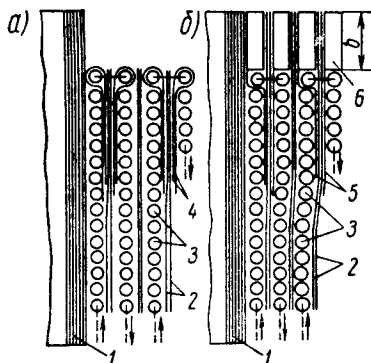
Междуслойная изоляция крепление крайних витков многослойной обмотки из круглого провода:
